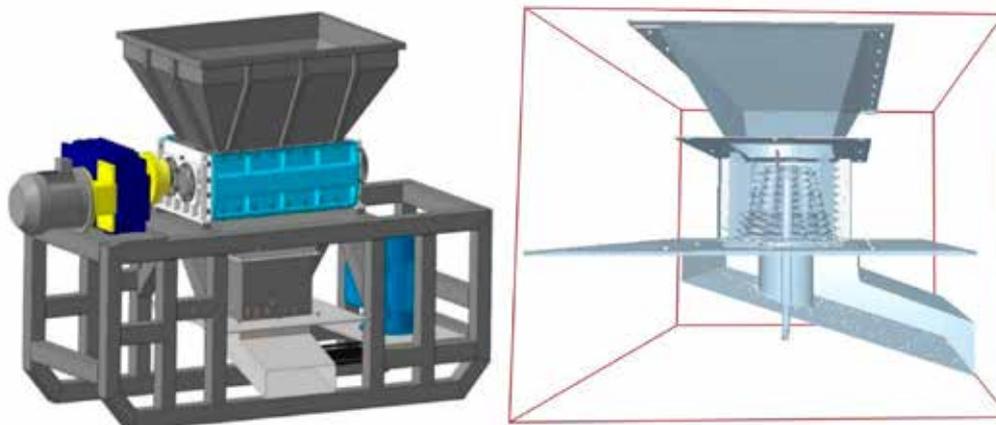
Цифровые модели: а – двухстадийный измельчитель; б – вторая стадия – камера домола с наборным многолезвийным инструментом и зубчатой рубашкой
